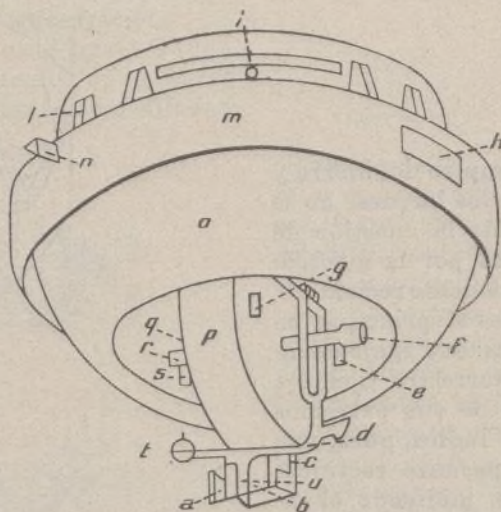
Croquis que muestra el dispositivo del aparato amortiguador.—a, b, agujero del tubo; c, tubo de escape; d, pieza que mantiene u vertical; e, engrasador; f, cojinete del eje; g, abertura de aspiración; h, anillo de suspensión á la cardan; i, anillo para asir la brújula; l, tornillo de posición; m, anillo de suspensión á la cardan; n, cuchilla del círculo exterior de la suspensión; p, caja que encierra el giróscopo; q, abertura de aspiración; r, cojinete del eje; s, engrasador; t, contrapeso; o, recipiente con mercurio.
